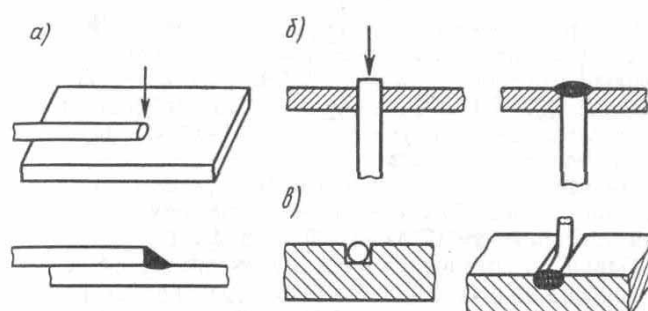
Типы соединений проволоки с массивными деталями:
